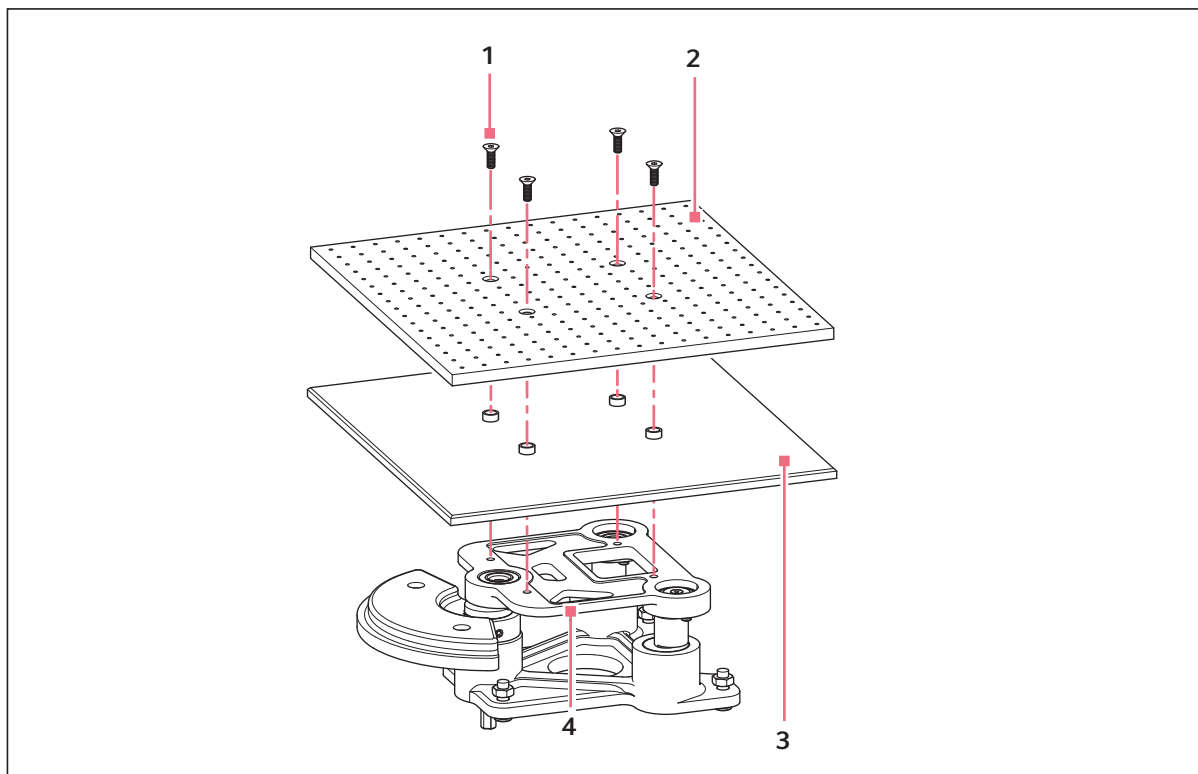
Установка платформы и крышки для защиты от брызг
